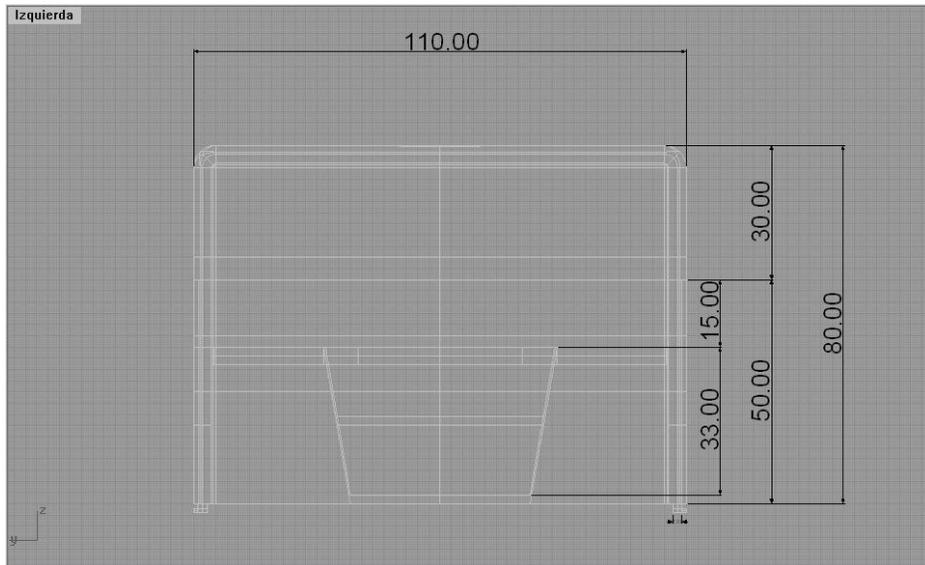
Vista frontal de la carcaza exterior superior 1:1 en mm.
